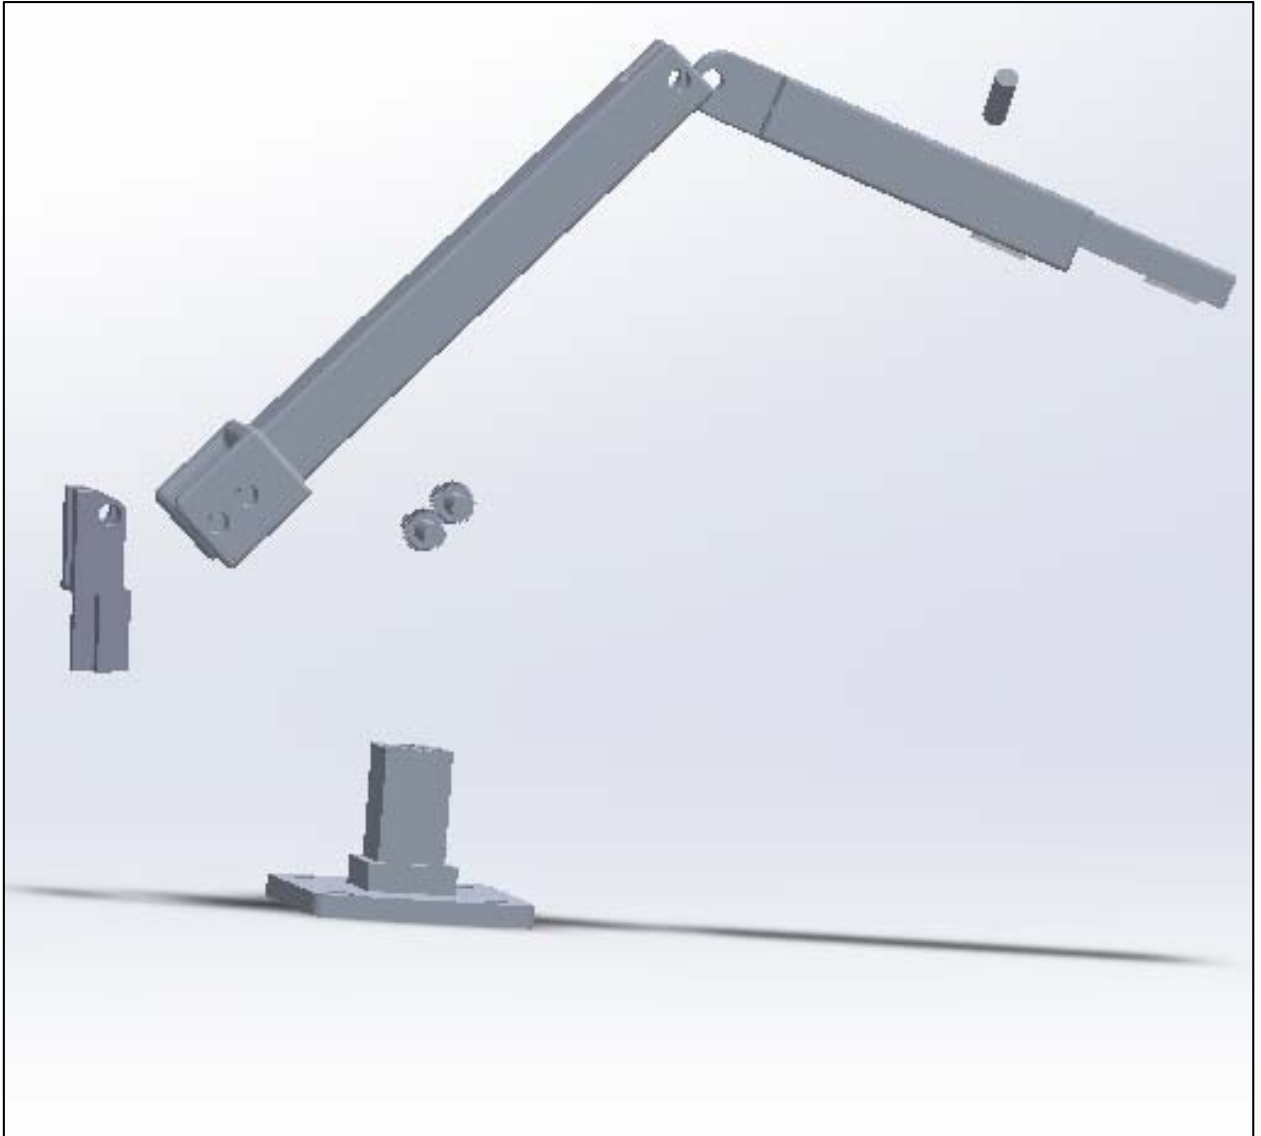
Vista lateral de elementos explosionados en Solidworks
